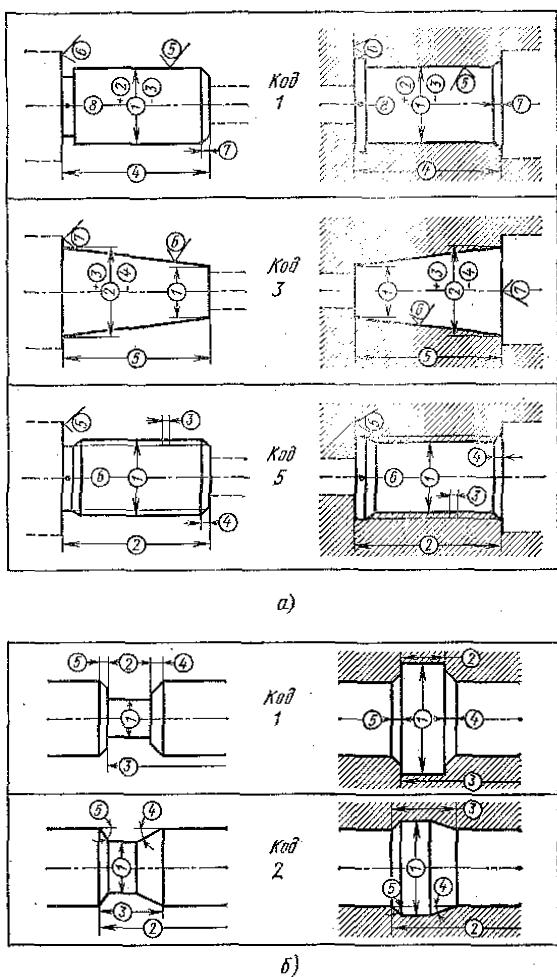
Основные и вспомогательные элементы описания детали и заготовки в MITURN
